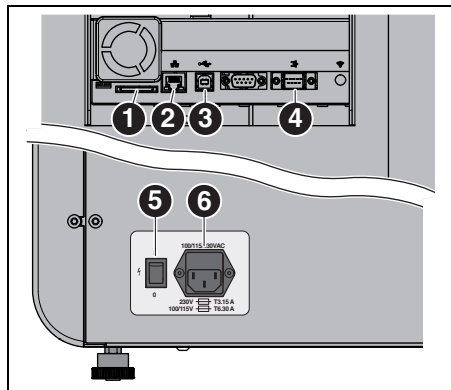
Interfaces sur la face arrière de la fraiseuse
